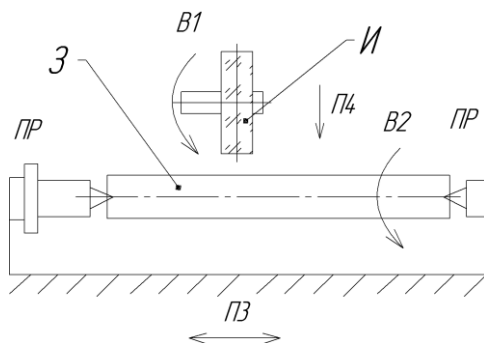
Эскиз рабочей зоны круглошлифовального станка:
